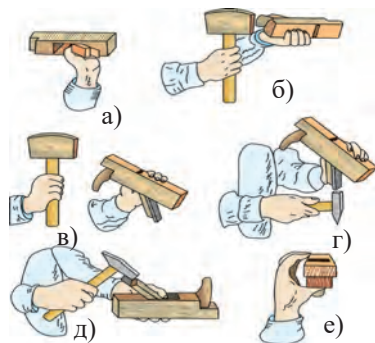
Выемка и установка лезвия при налаживании рубанка к работе: а, б – при выемке лезвия рубанок нужно держать следующим образом; в, г – установка лезвия в рубанок; д – закрепление клина; е – проверка правильного установления лезвия.
